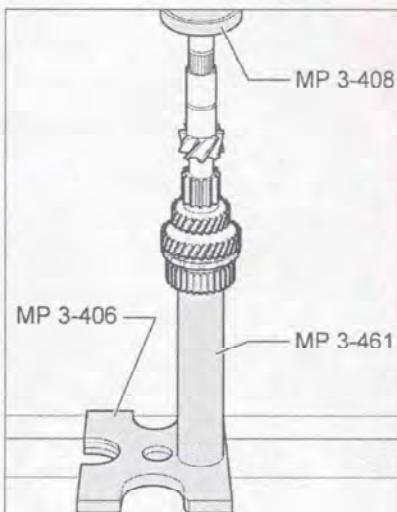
Установка ступицы синхронизатора 3-й/4-й передач.
